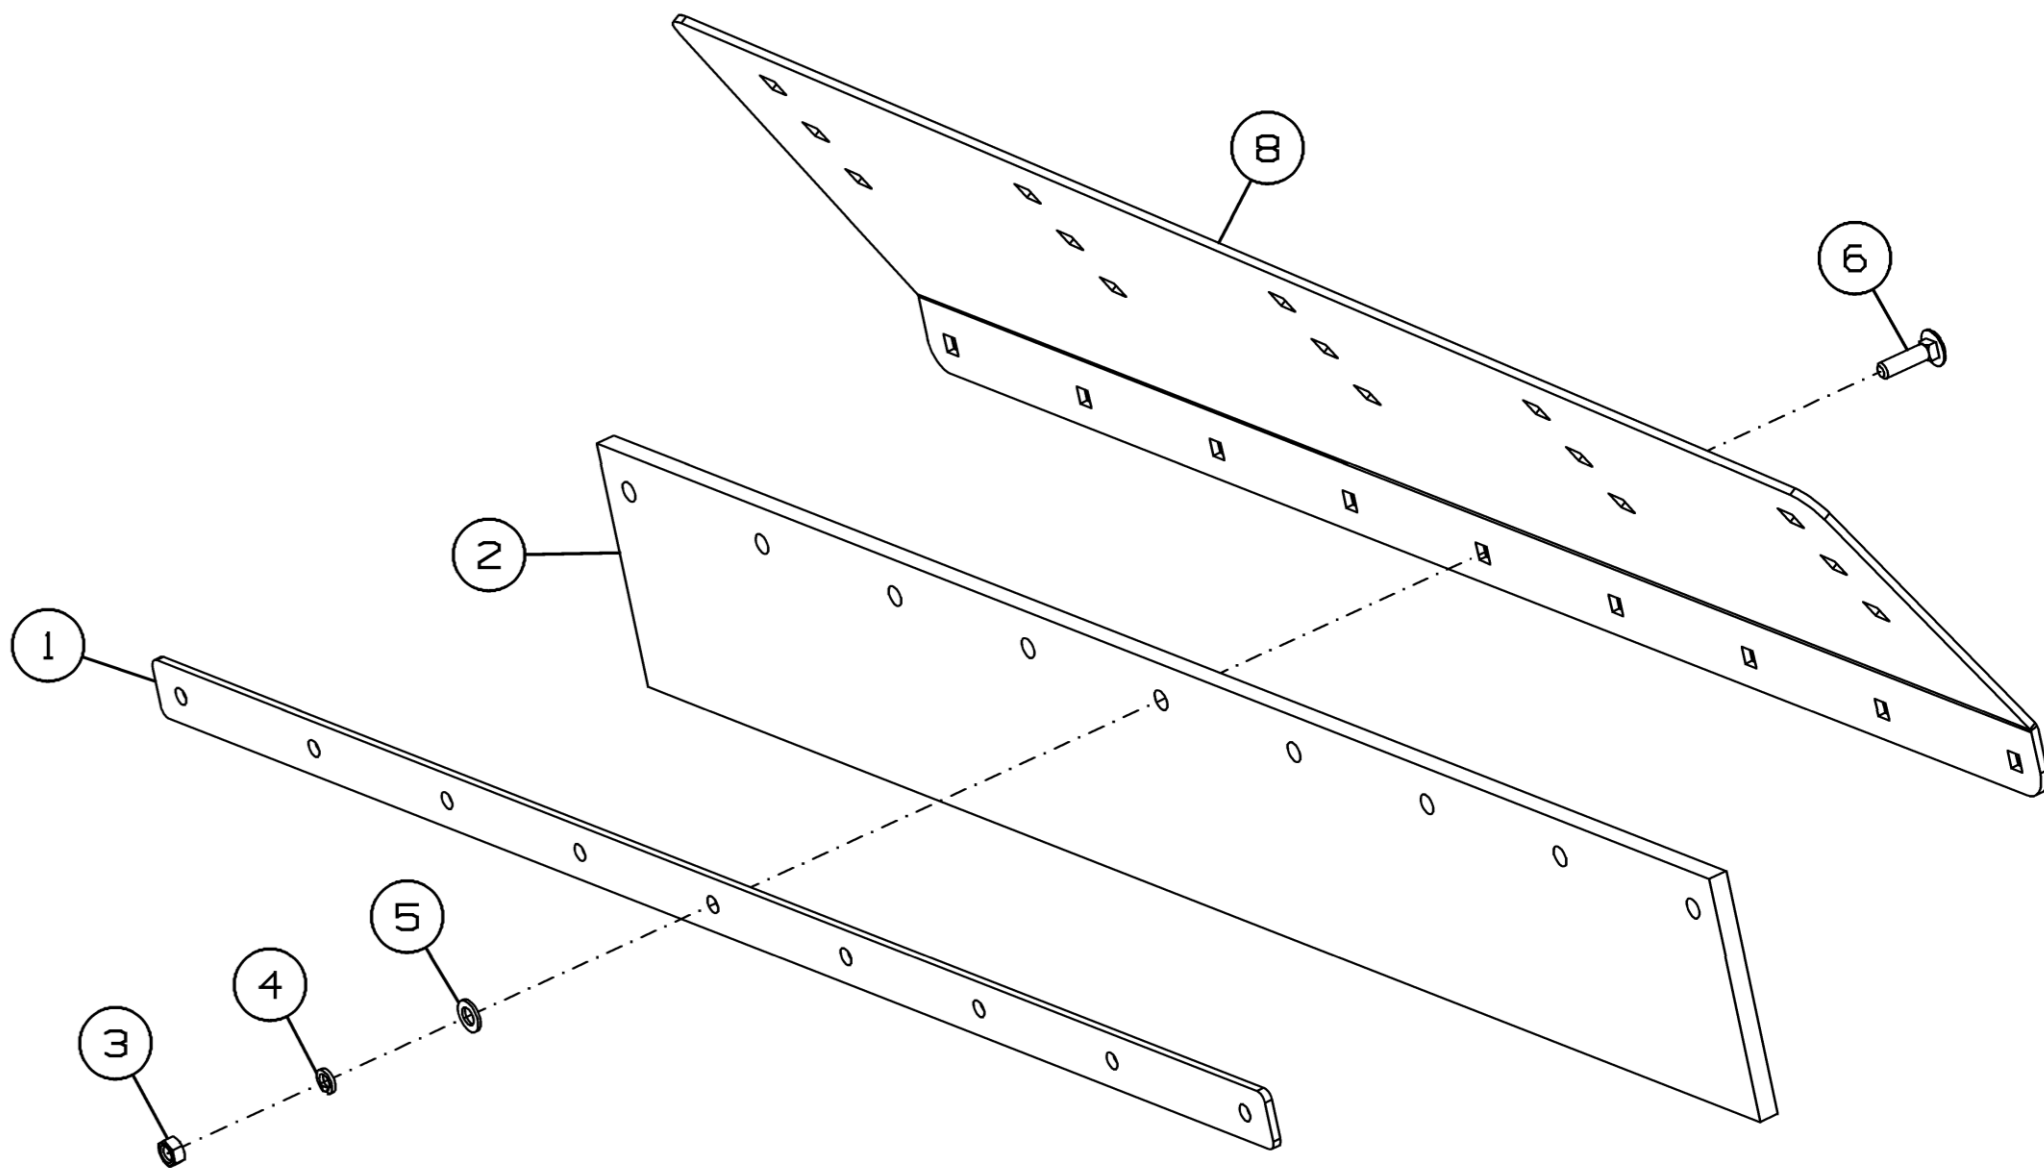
Дополнительный щиток валкообразователя GM-500R.06.01.140-01
